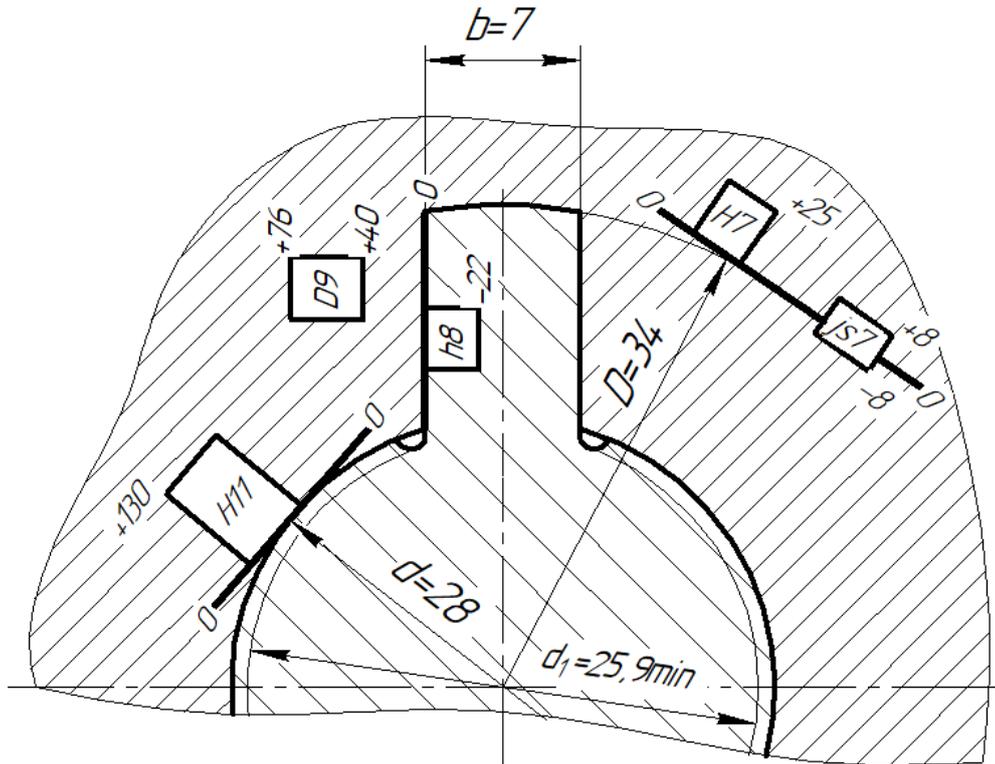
Схема полей допусков шлицевого соединения
